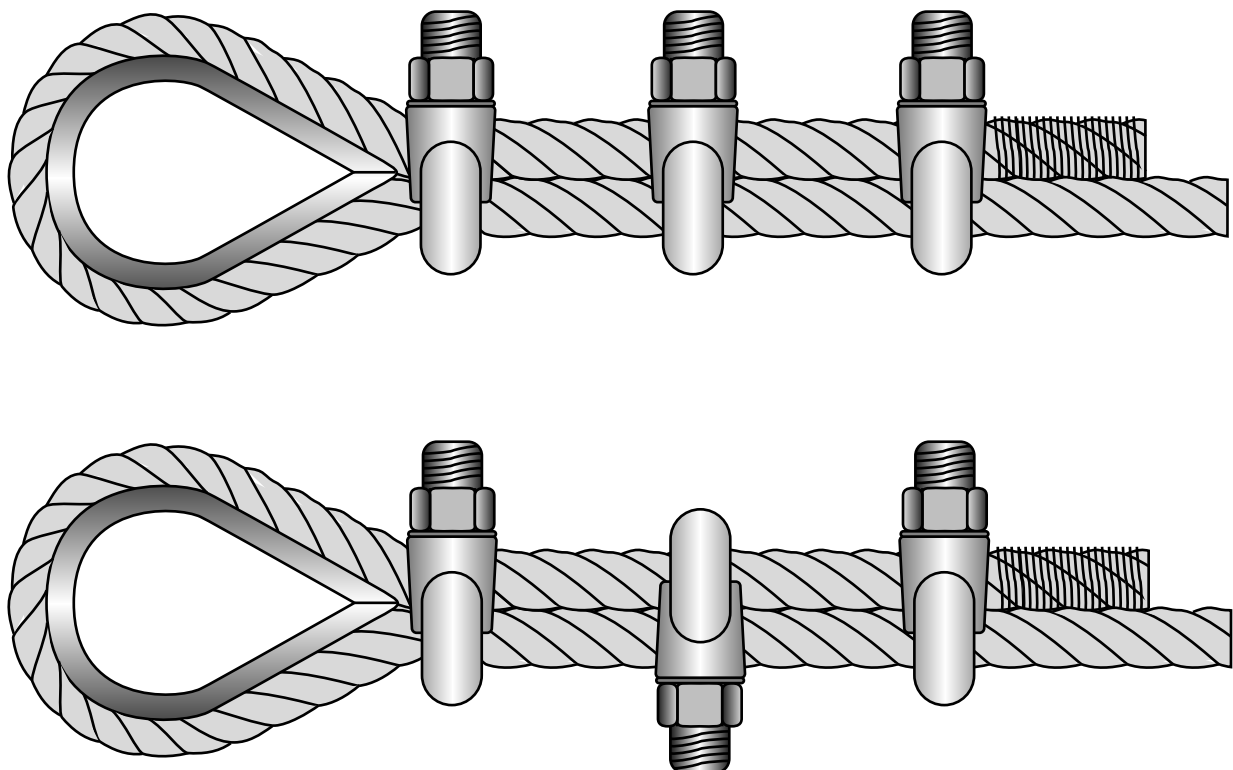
Unsachgemäß ausgeführte Endverbindungen mit Drahtseilklemmen
